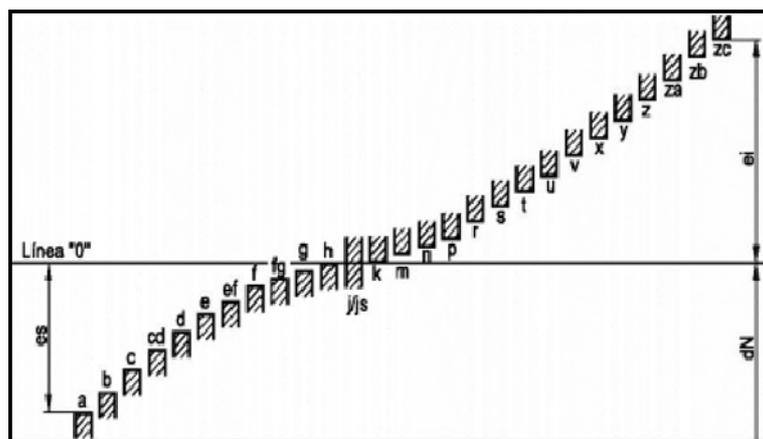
Posiciones de las Tolerancias para Ejes
